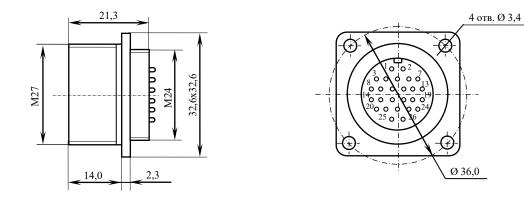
Габаритные и установочные размеры блочной розетки на 26 контактов
